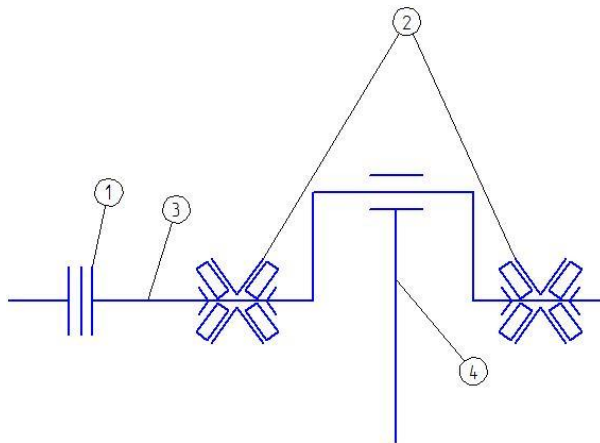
Кінематична схема вузла колінчастого валу : 1 - муфта; 2 – підшипник 3003752; 3 – вал колінчастий; 4 – штовхач
